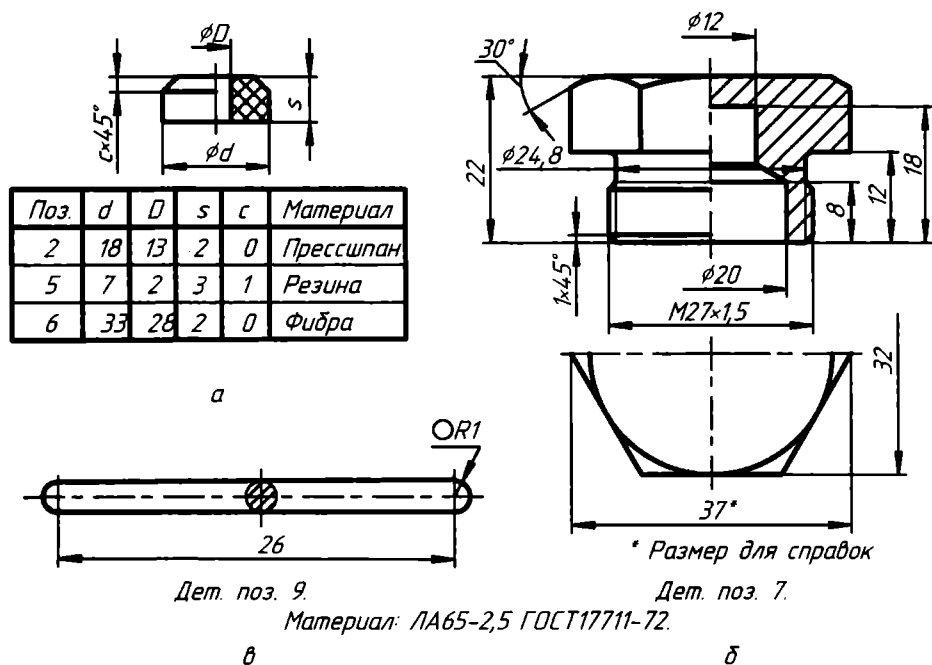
Чертежи: а — прокладок; б — пробки; в — штока
